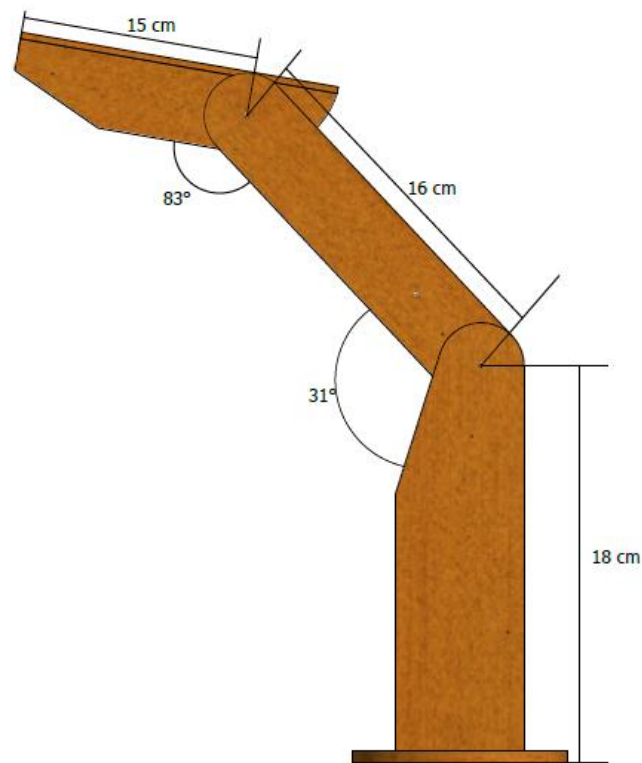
(b) – Dimensões para cálculo da cinemática direta. Fonte: autores.
